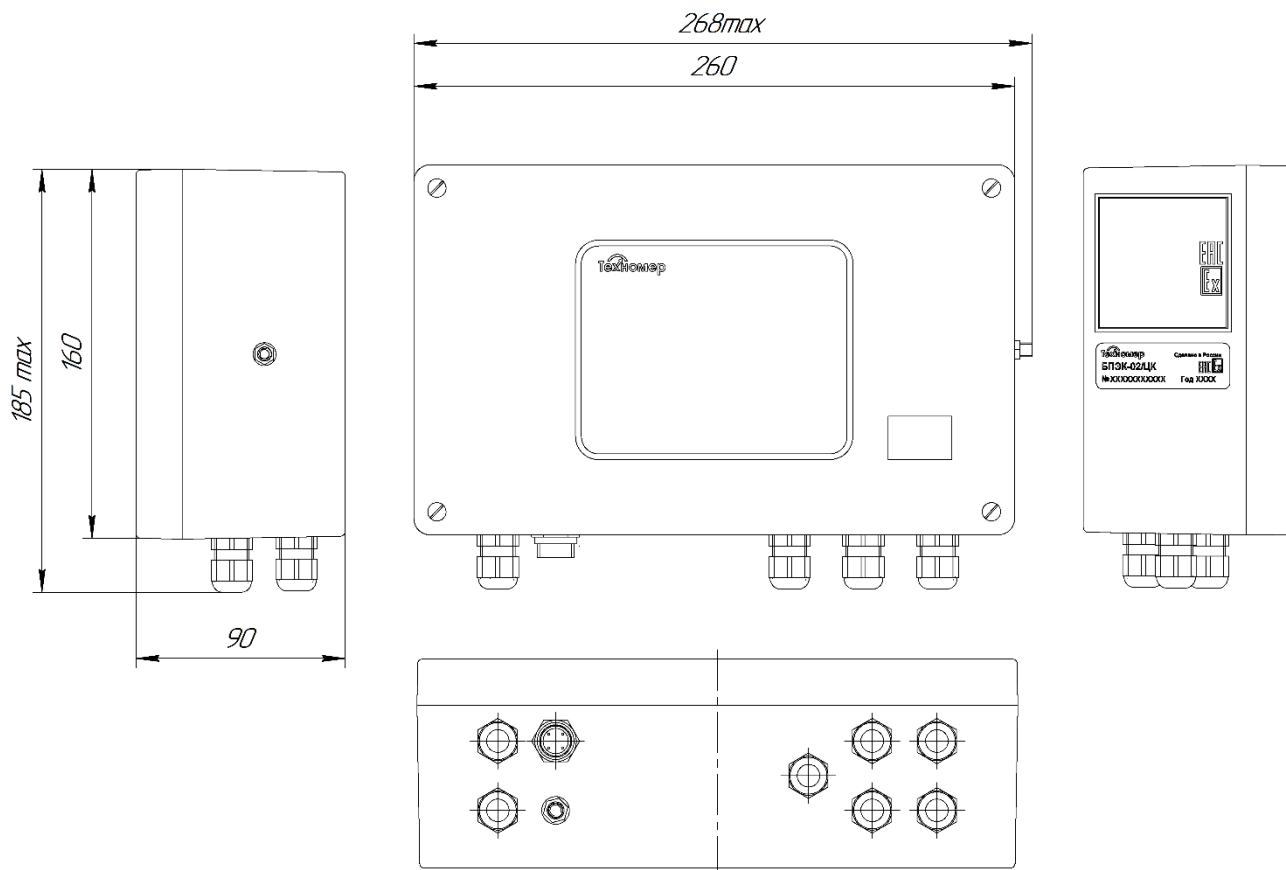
Габаритные размеры блока БПЭК-02/ЦК
